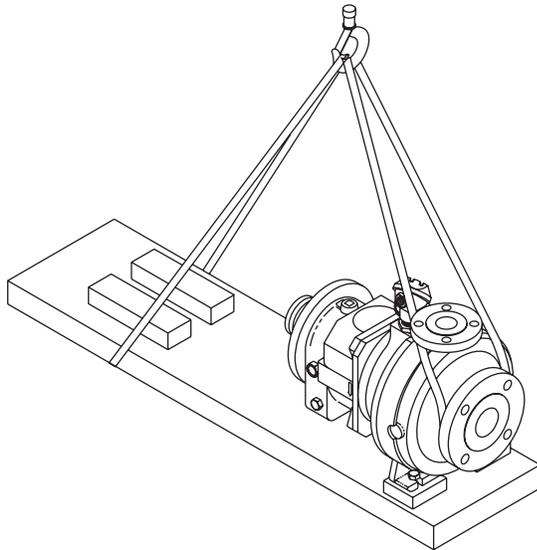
Metodo di sollevamento corretto per una pompa con una base e senza motore
